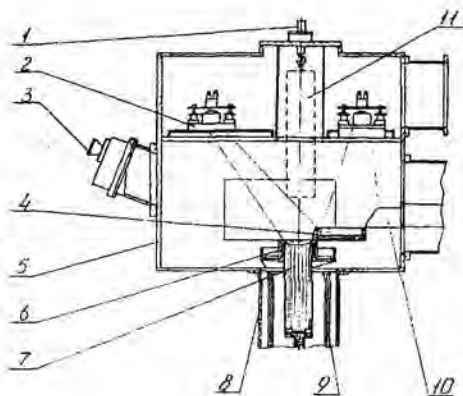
Схема електронно-променевої установки UE-174: 1 — механізм вертикальної подачі; 2 — електронно-променевий нагрівач; 3 — пристрій для спостереження; 4 — проміжна ємність; 5 — робоча камера; 6 — водоохолоджувальний кристалізатор; 7 — виплавлений зливков; 8 — механізм формування та витягування зливка; 9 — теплоізоляційні екрани; 10 — бічний механізм подачі шихтових матеріалів; 11 — переплавленна заготовка.
